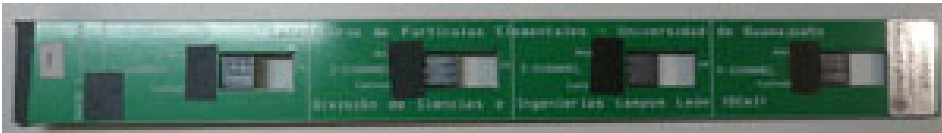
Tarjeta-F manufacturado, vista en la cara inferior con conector Mini-DIM
